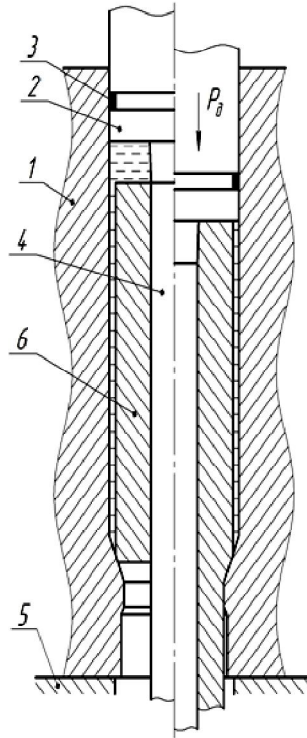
Схема гидропрессования трубчатых заготовок на оправке
